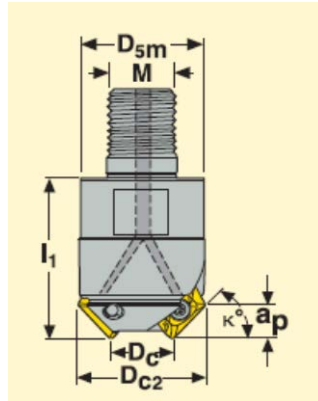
Фреза фасочная R217.49–1684.RE-ХО12-45.3А
